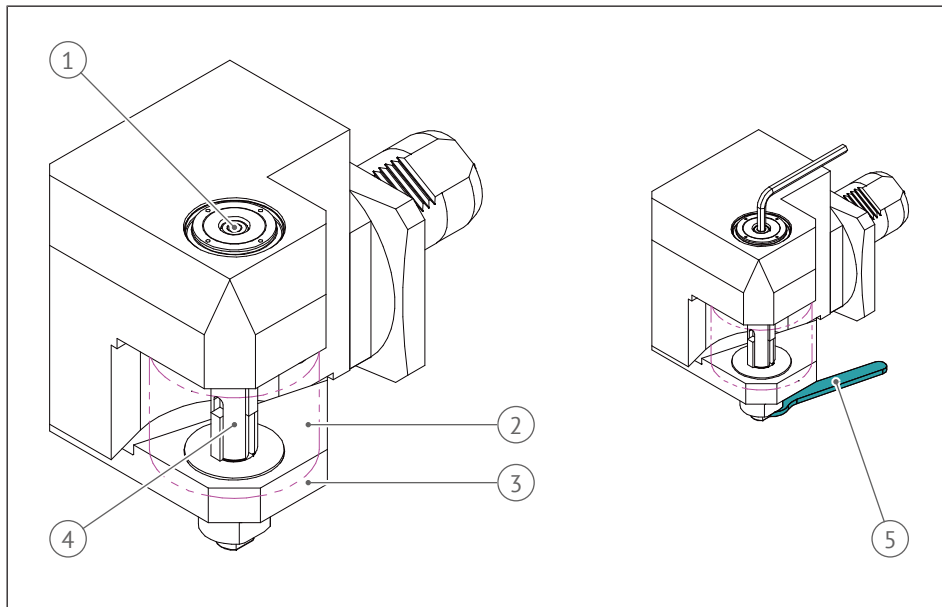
Scheibenfräserkopf mit austauschbarer Fräserwelle
